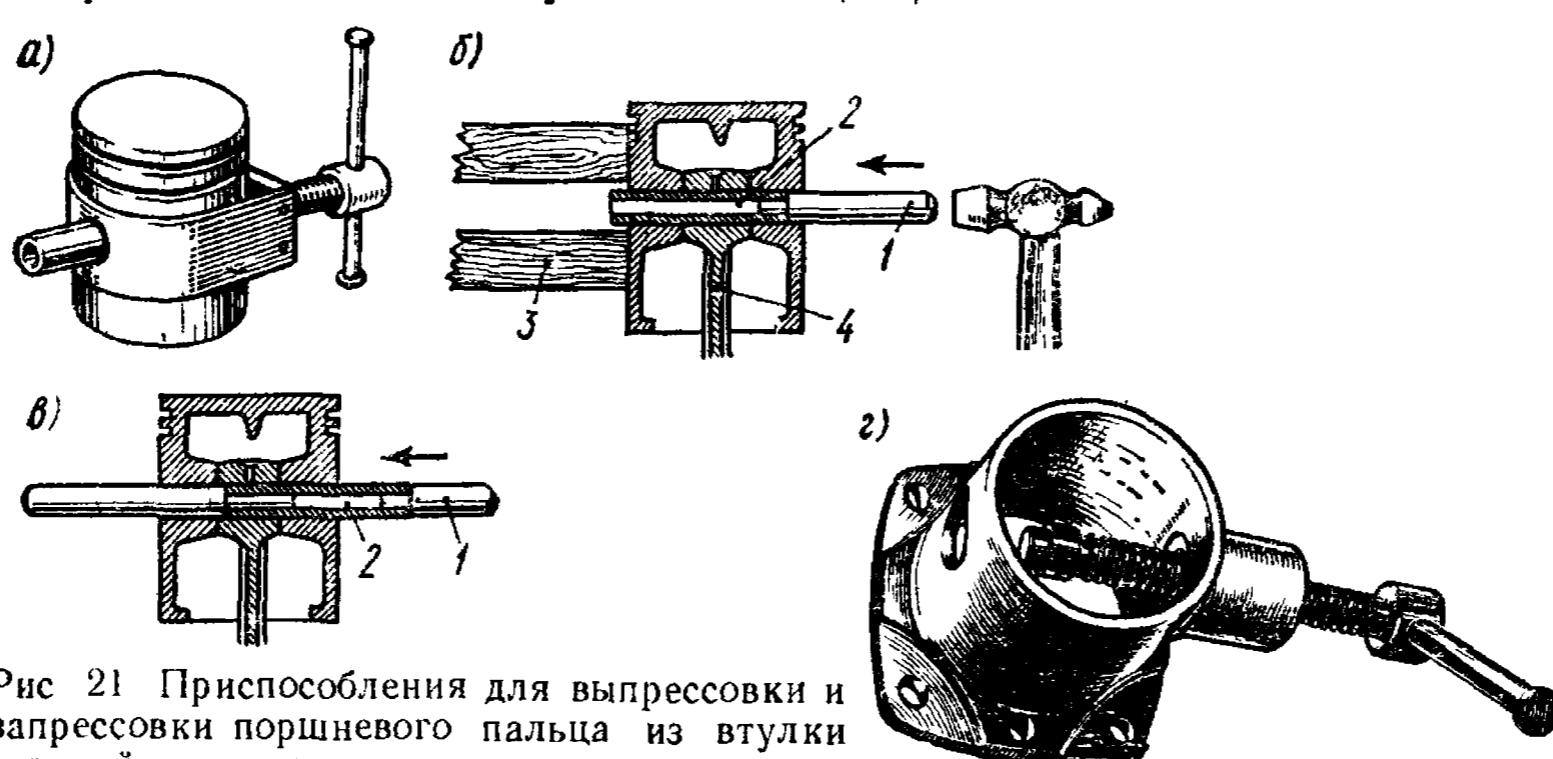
Приспособления для выпрессовки и запрессовки поршневого пальца из втулки верхней головки шатуна: а — ленточное приспособление; б, в — выполнение операций с помощью оправки и молотка; г — специальное приспособление;
